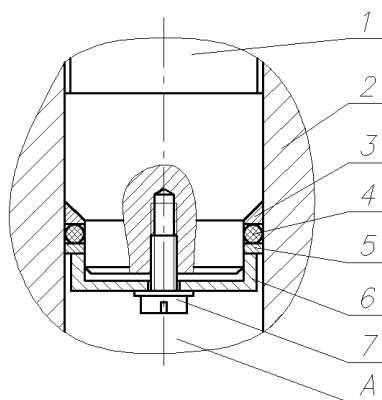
Конструкция уплотнения плунжера: 1 – плунжер; 2 – вискозиметр; 3 – медная прокладка; 4 – резиновое уплотнение; 5 – стальная шайба; 6 – нажимная крышка; 7 – винт
